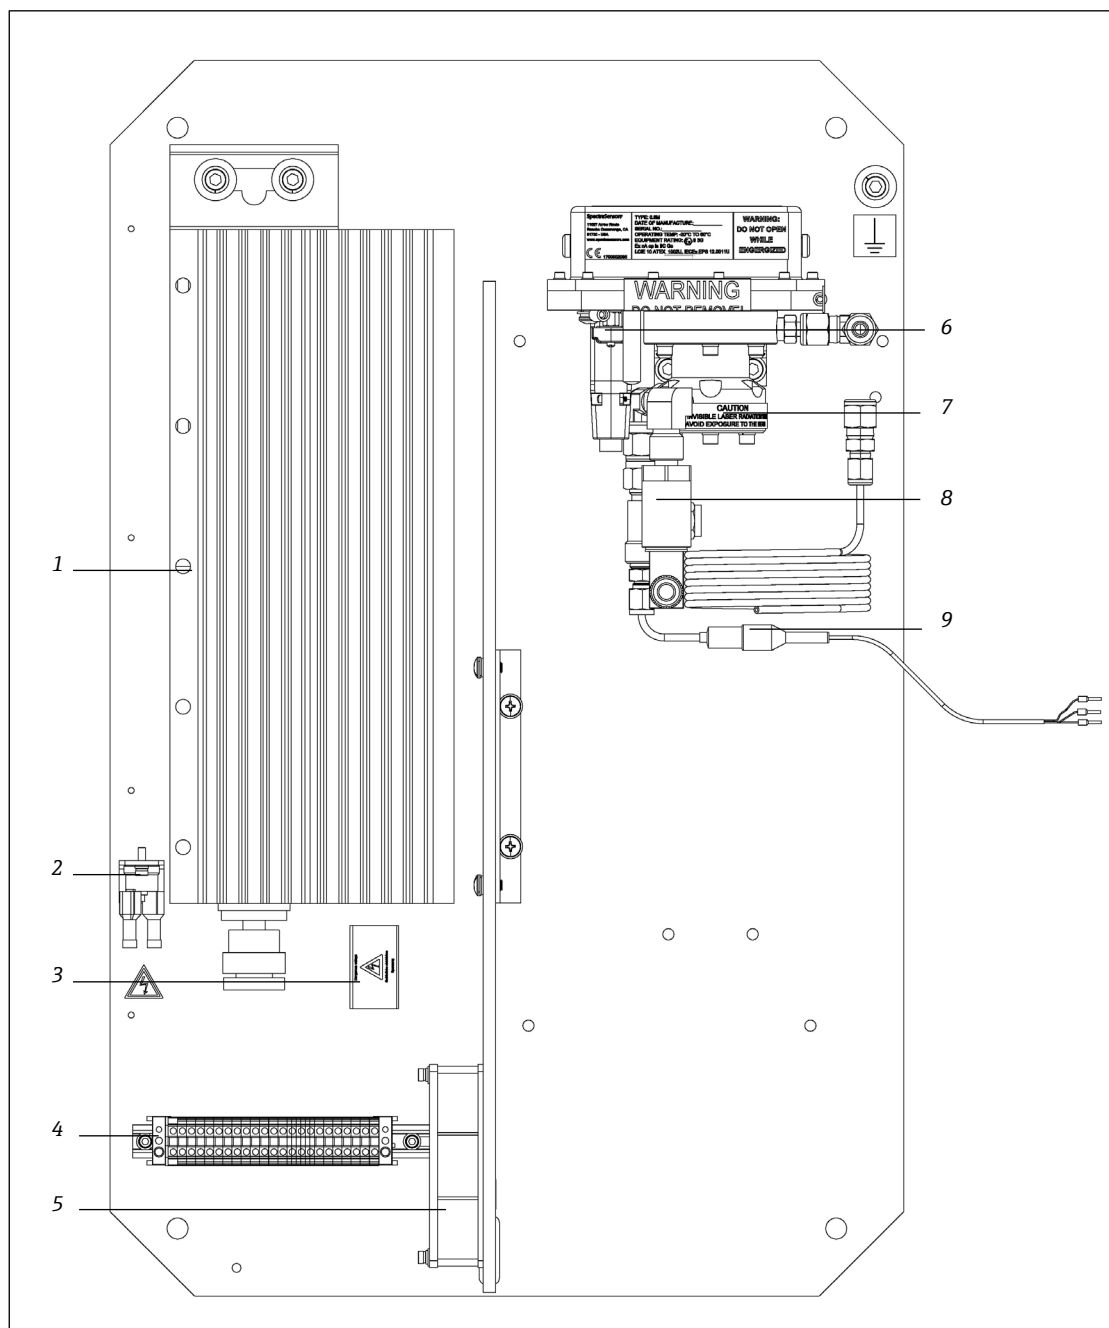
Komponenten in einem 0,1m-Messzellengehäuse
